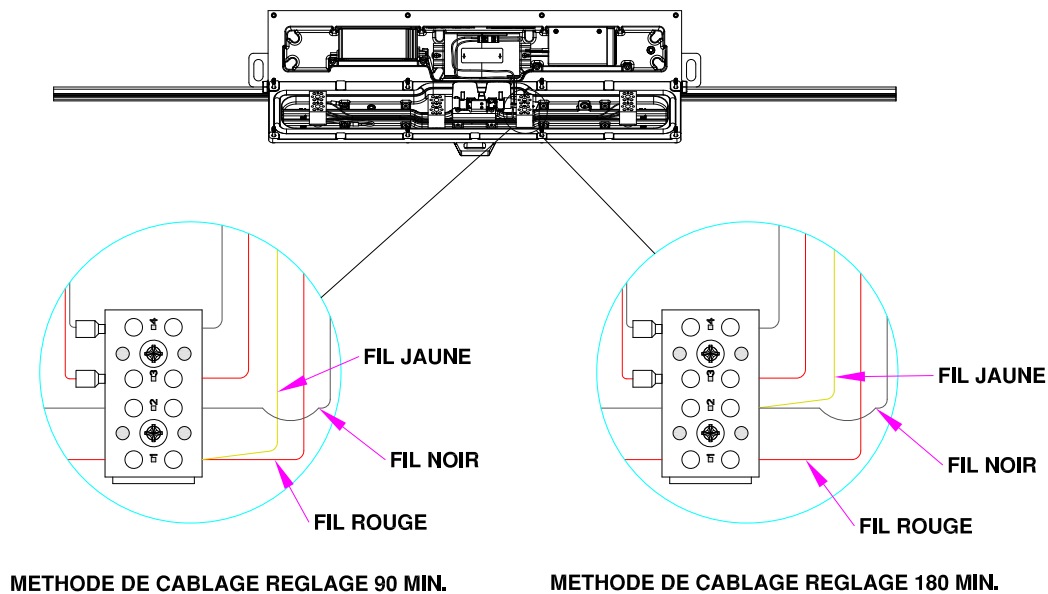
MÈTHODE DE CÂBLAGE POUR RÉGLER LA DURÉE
